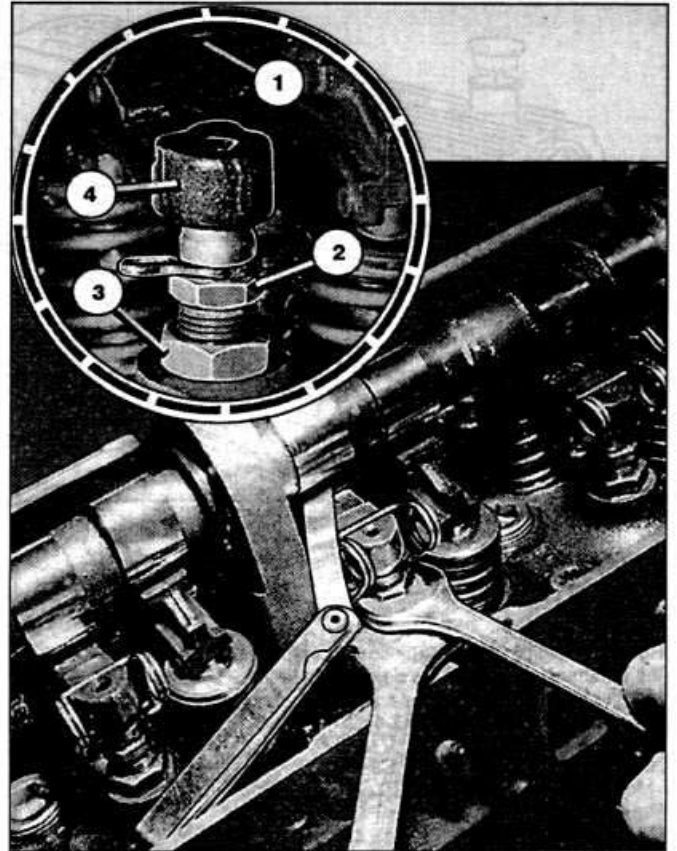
Регулировка зазора в механизме привода клапанов:
